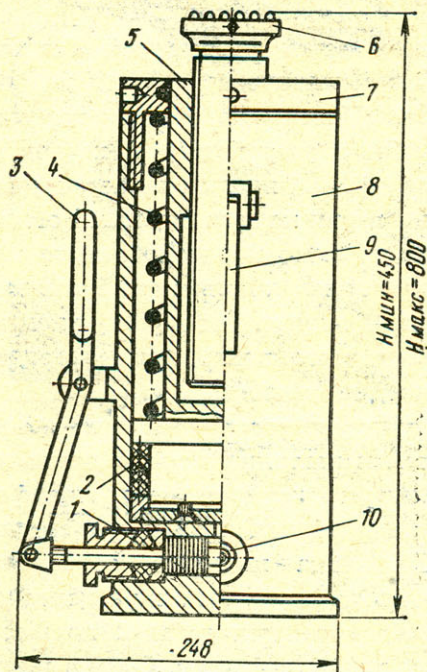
Домкрат-богатырь: 1 — золотник; 2 — уплотнение штока; 3 — рукоятка; 4 — пружина; 5 — шток; 6 — винт; 7 — гайка; 8 — корпус; 9 — откидная ручка (две); 10 — штуцер.
